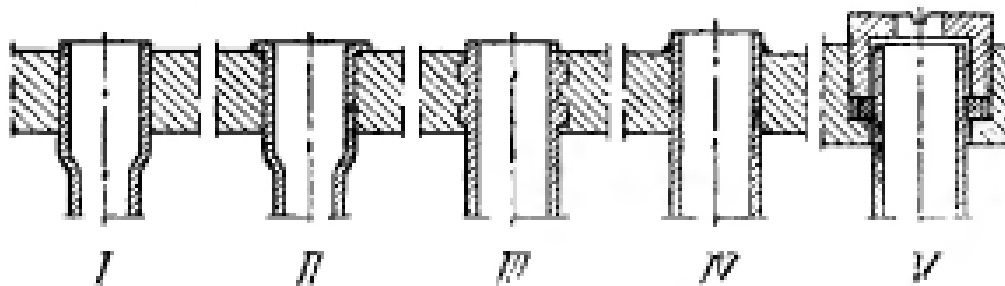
Закрепление трубок в трубных решетках: I, II, III—развальцовкой; IV—сваркой; V—сальниковым соединением.
